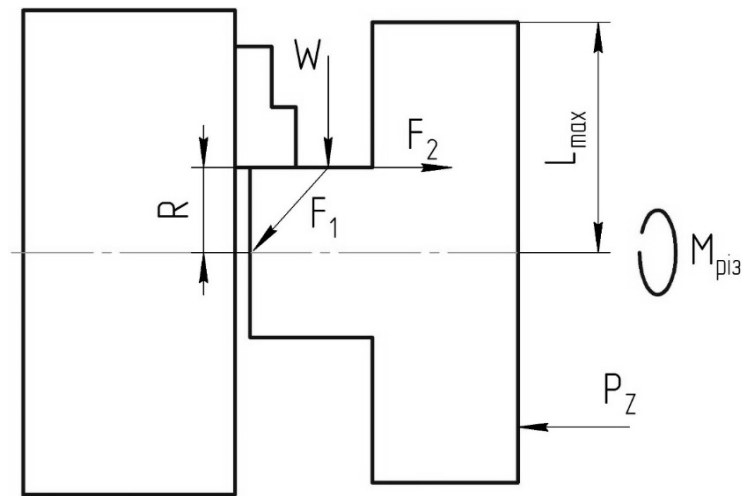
Розрахункова схема для визначення зусилля затискання
